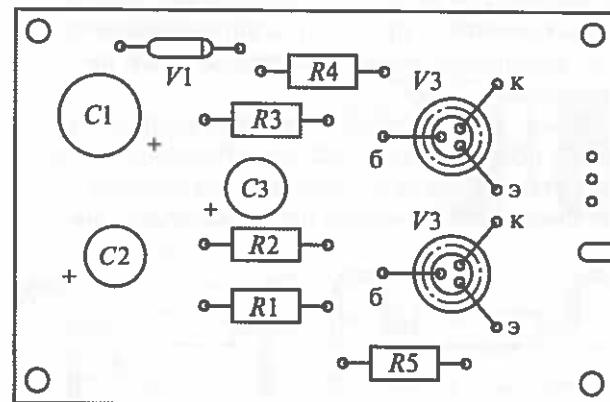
Пример монтажной схемы электронного устройства на печатной плате
